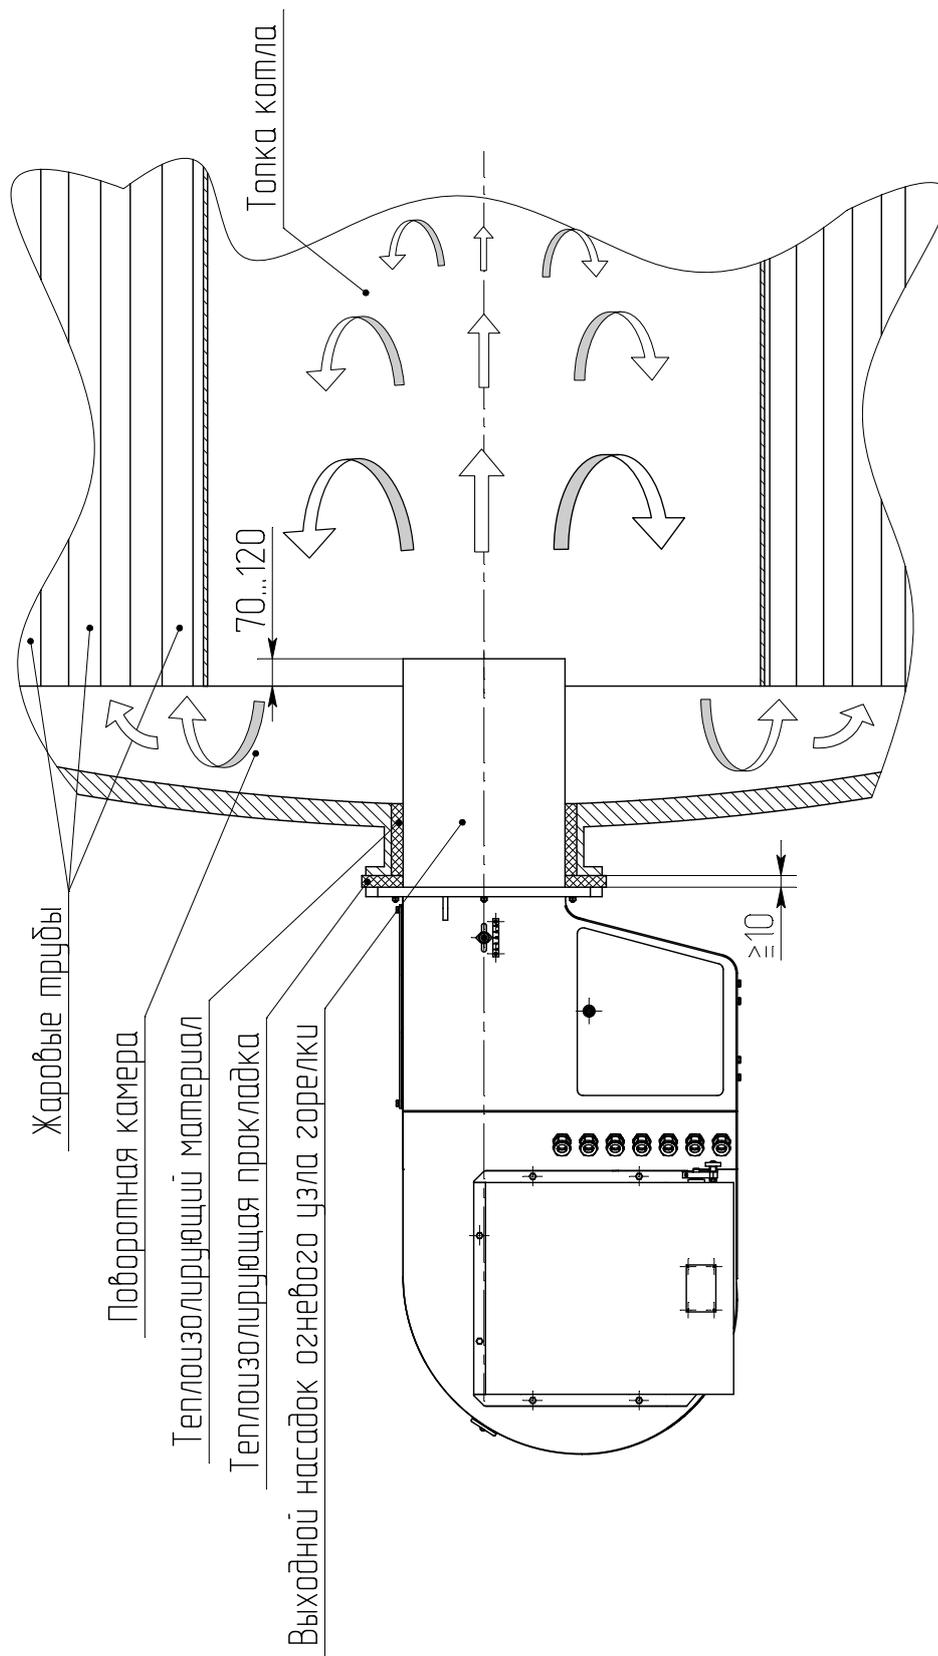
Установка горелки на теплоагрегат с реверсивной топочной камерой
